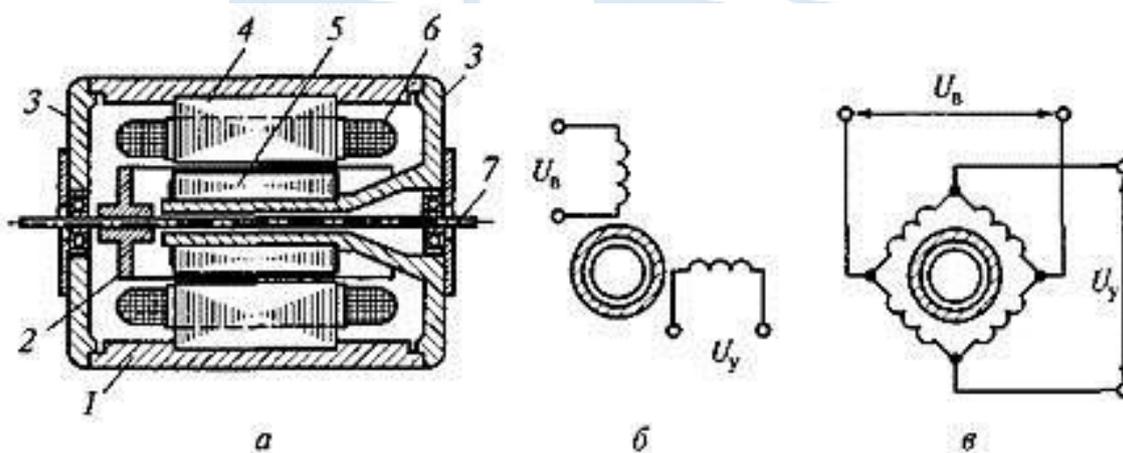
Конструкция асинхронного исполнительного двигателя с полым немагнитным ротором:
